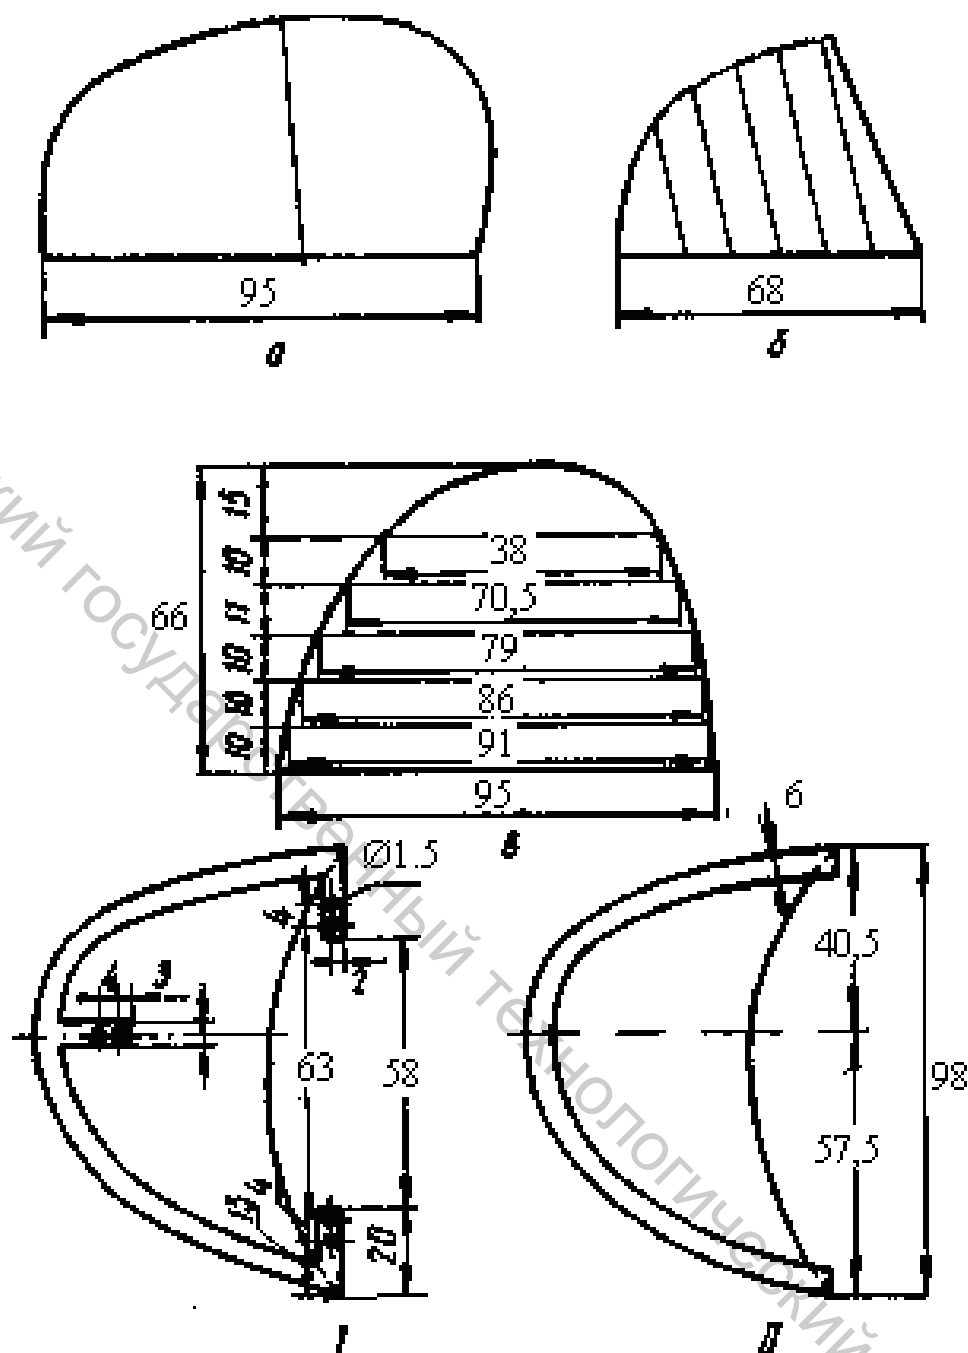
Шаблоны и общий вид наружного и внутреннего металлических подносков: *а* – поперечное сечение; *б* – продольное сечение; *в* – след; *I* – наружный носок; *II* – внутренний поднос
